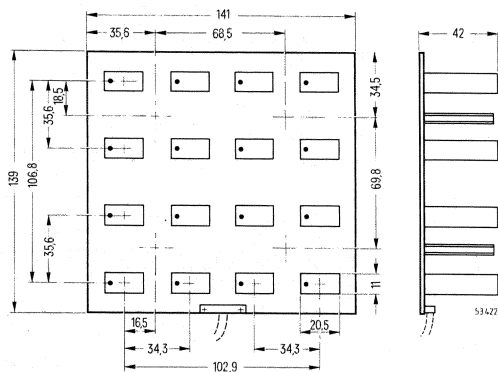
Tastenfeld für Zeit-/Zählerbaugruppe 383
